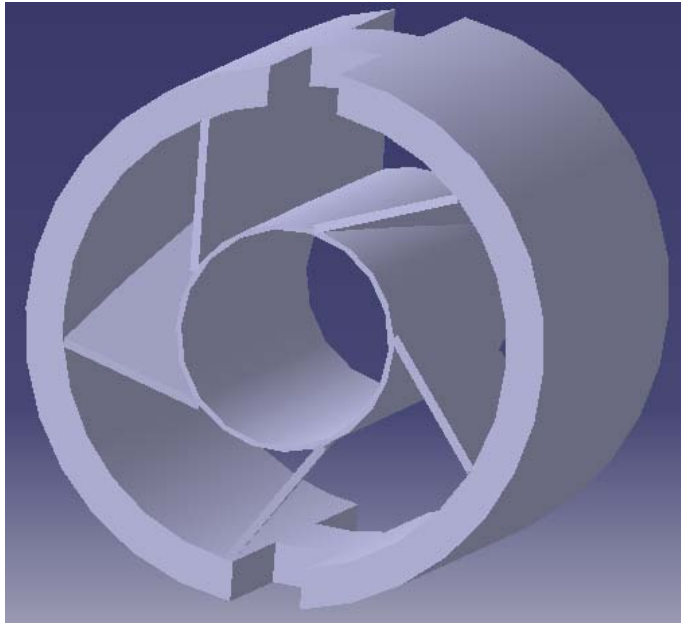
Conjunto completo del rodete o rotor de la turbina.
